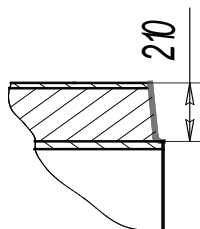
Места зачистки свариваемых поверхностей
